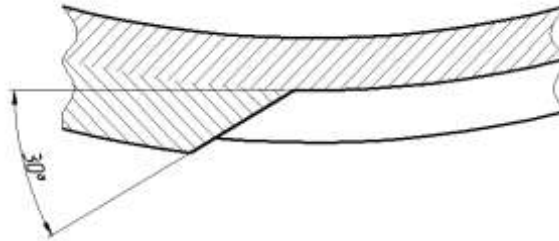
Загальний вигляд зачистки зони початку зварювання
